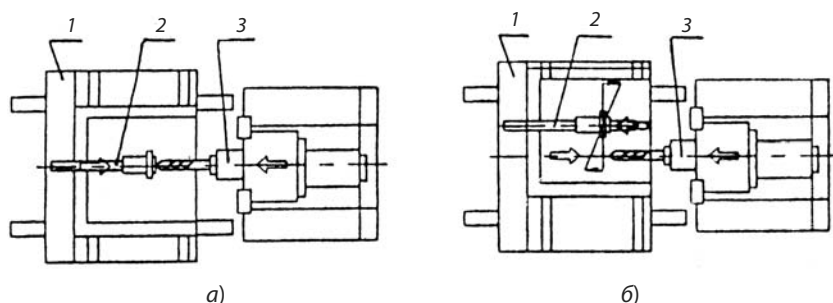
Компоновка станка с ЧПУ с центральным (а) и смещенным (б) расположением ходового винта привода поперечной подачи салазок
